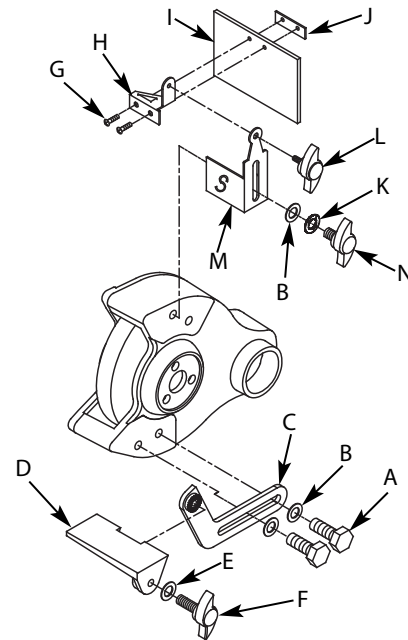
Soporte de la Herramienta Izquierdo y Conjunto de la Protección de Ojos
